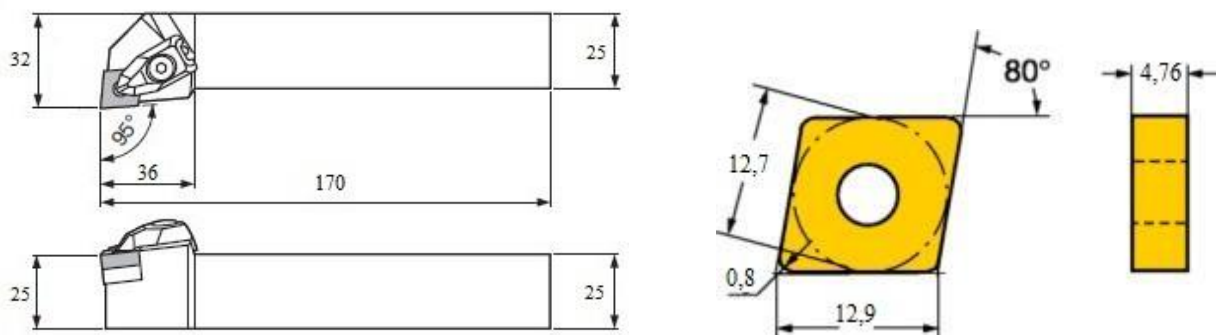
Проходная державка DCLNR 2525M 12 – пластина CNMG 12
